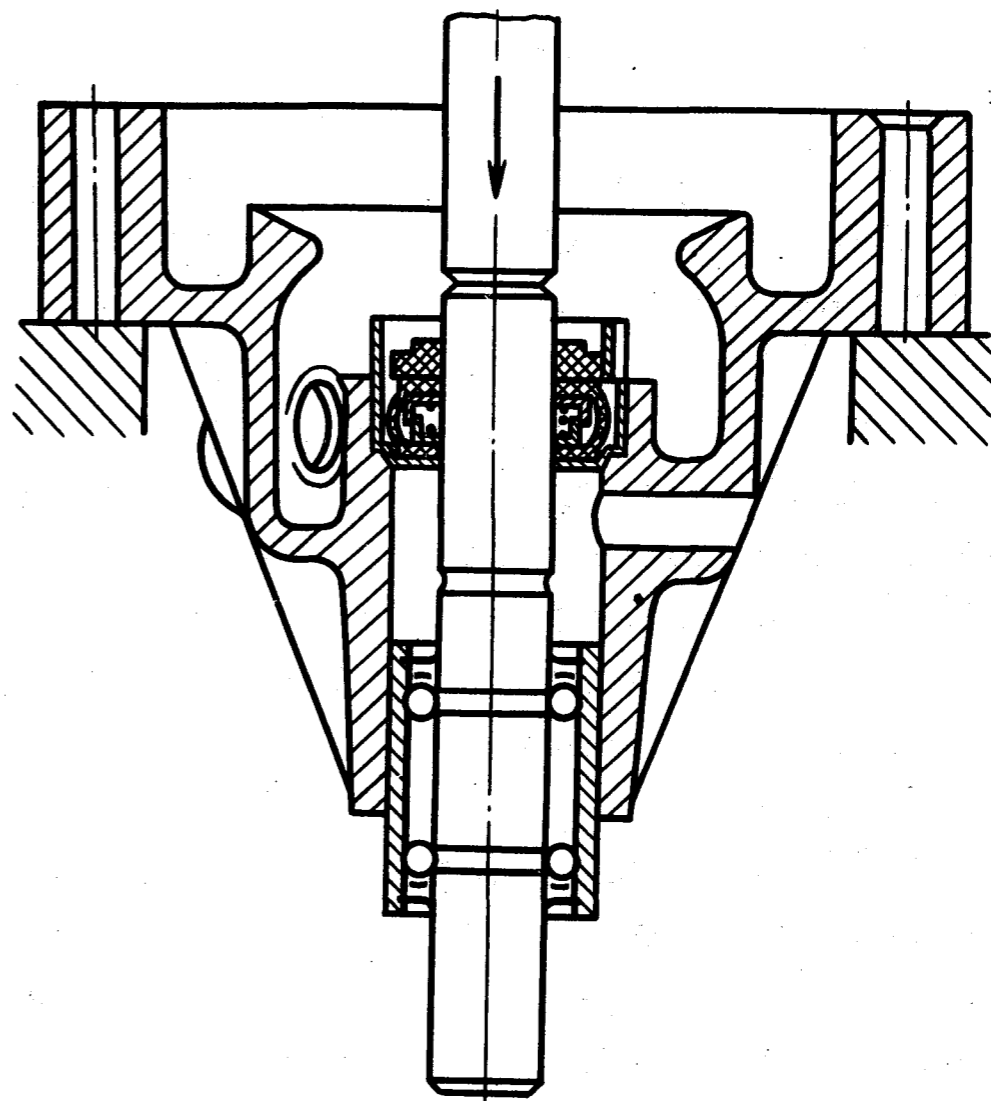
Выпрессовка подшипника с валом водяного насоса
